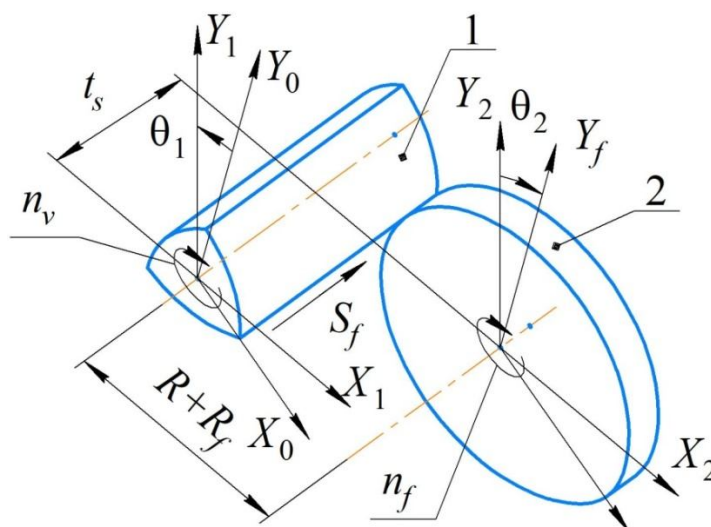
Схема обработки длинного вала с РК-профилем фрезой с конструктивной радиальной подачей
